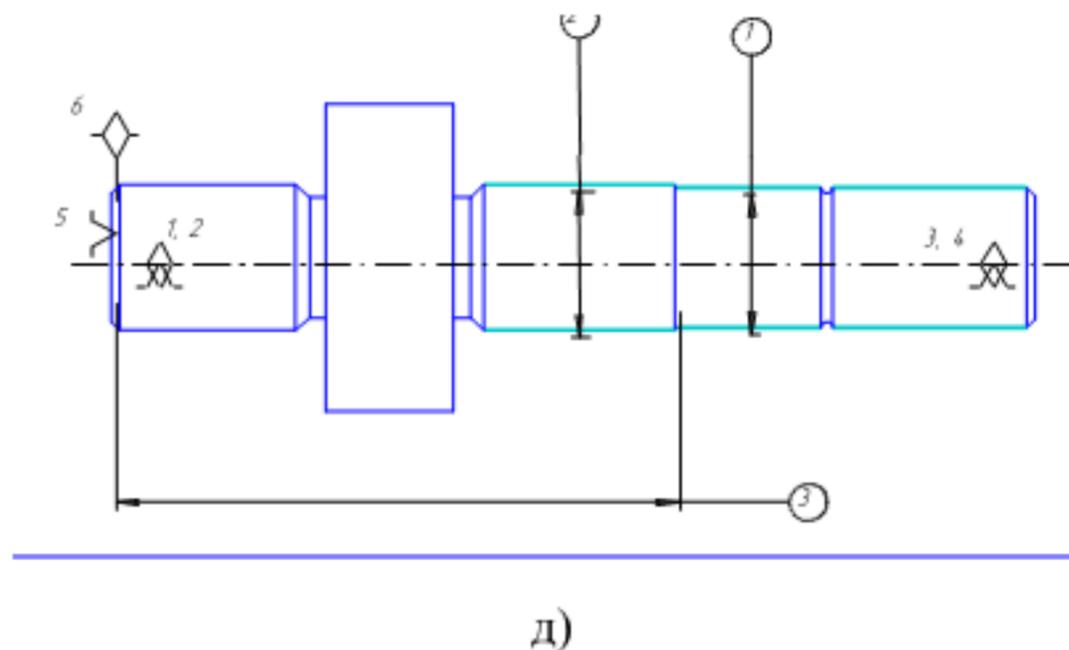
Схеми базування та обробки на верстатах токарної групи:
